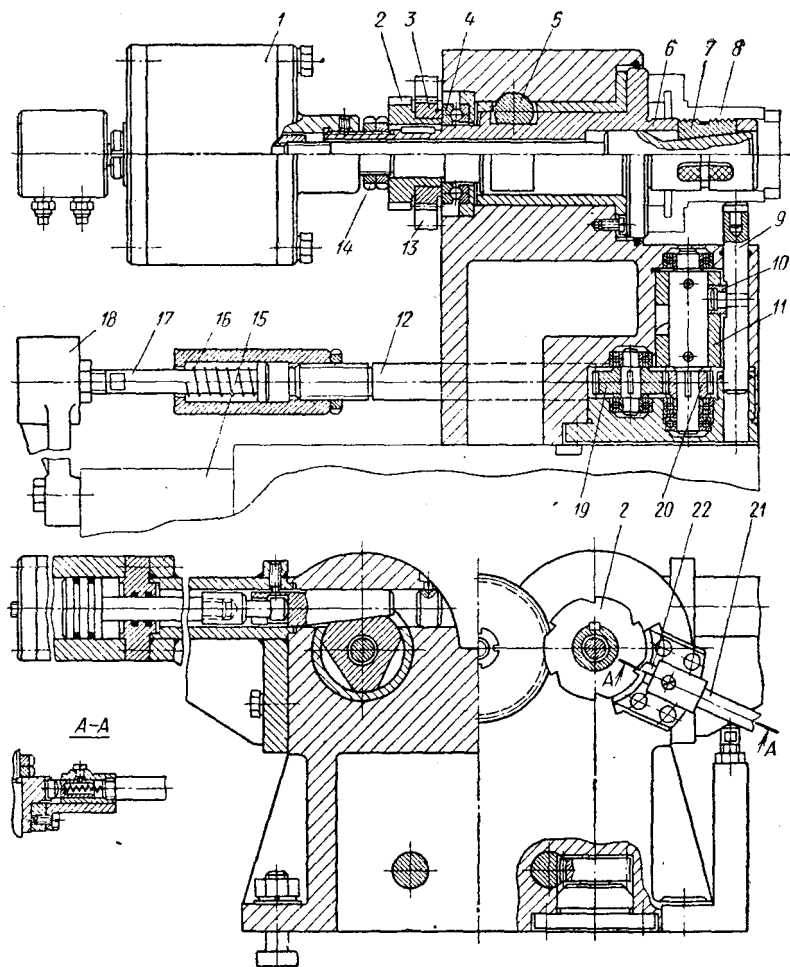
Автоматизированное приспособление для обработки зубьев полушестерен на вертикально-протяжных станках
